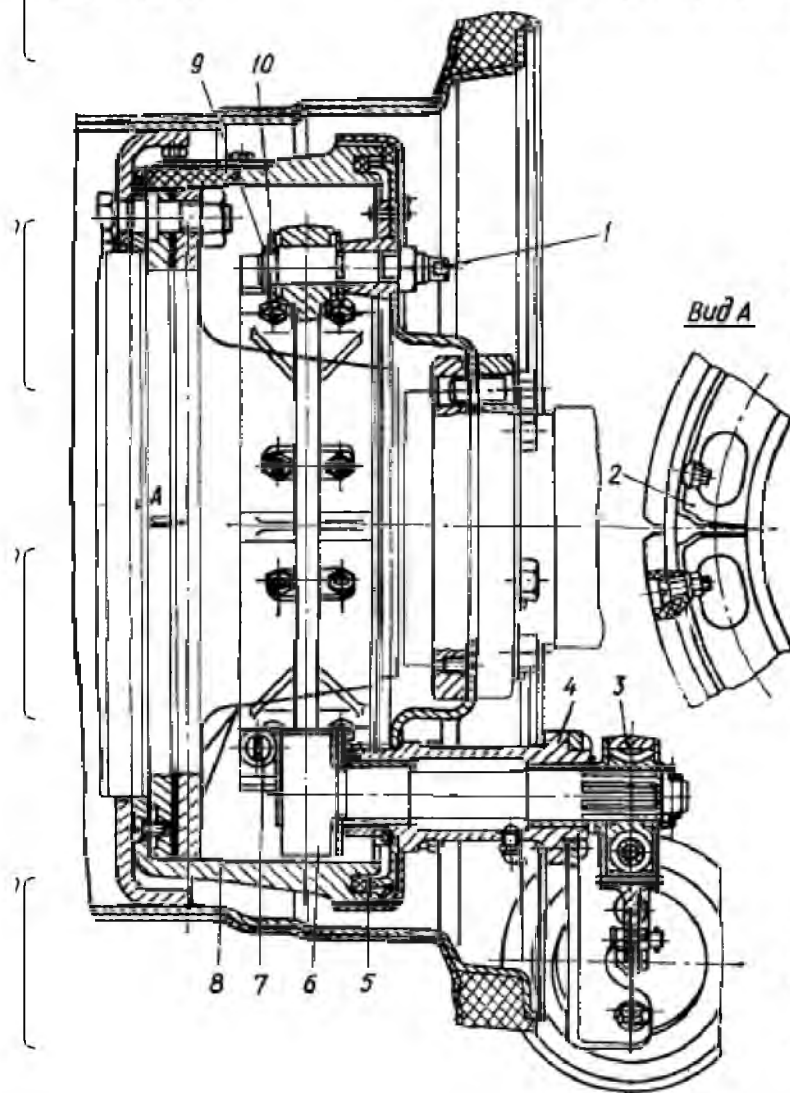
Колісне гальмо: 1 - ексцентрична вісь колодок; 2 - колодка; 3 - регулювальний важіль; 4 - кронштейн розтискного кулака; 5 - щит; 6 - розтискний кулак; 7 - стяжна пружина; 8 - гальмівний барабан; 9 - шайба; 10 - прокладка.
